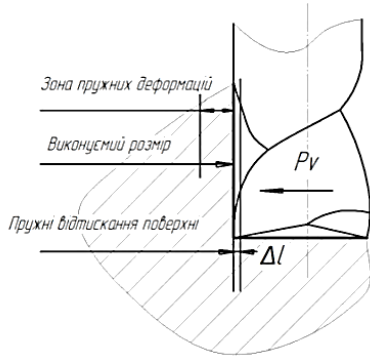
Схема взаємодії кінцевої фрези та матеріалу заготовки з пластмаси: P_y – сила різання, що діє нормально до поверхні; B – ширина зрізаного шару; D – діаметр фрези; Δl – величина пружних відтискань поверхні заготовки; S – подача верстата
